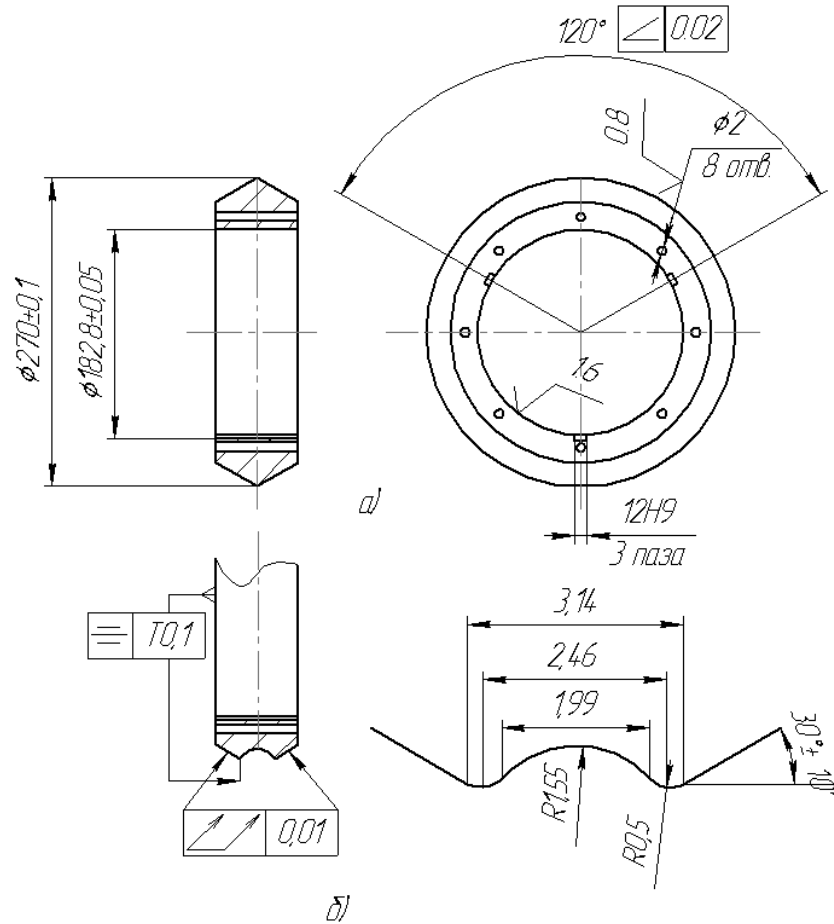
Валок трехвалковой клетки: а) до профилирования; б) профиль валака, получаемый точением
